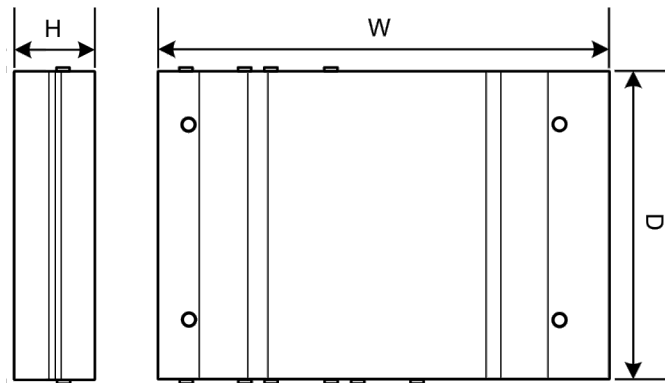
Skematisk fremstilling, dimensioner i millimeter
